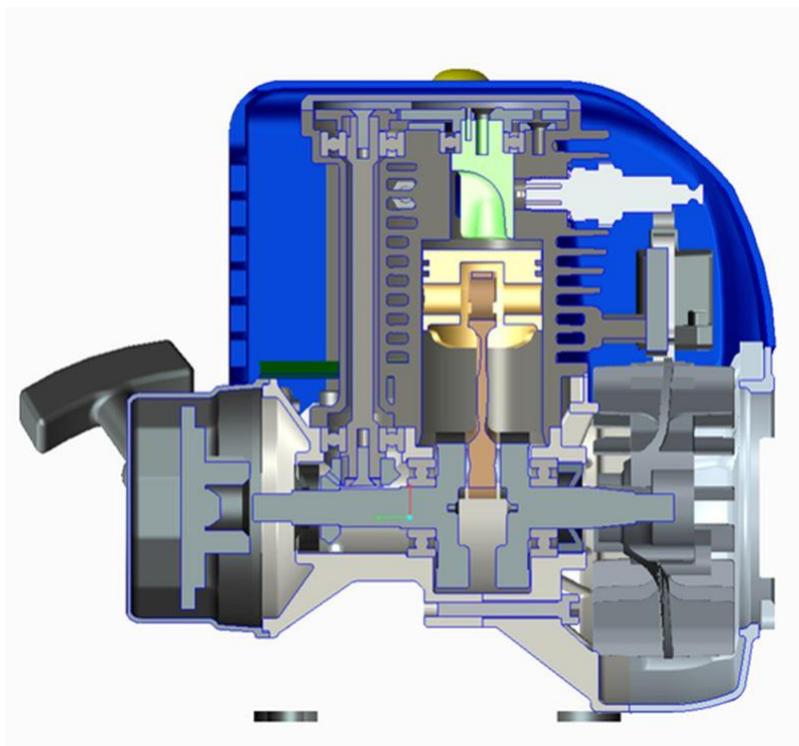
Двигатель для привода бытового механизированного инструмента и электрогенераторов.
